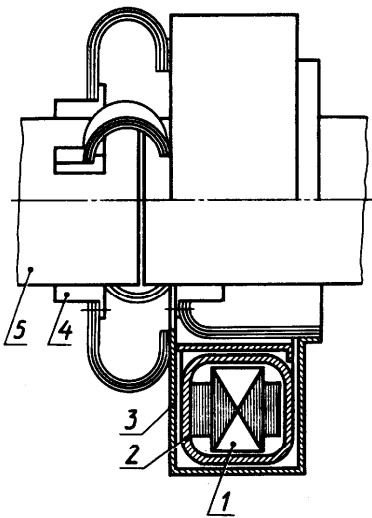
Кольцевой сварочный трансформатор для стыковой сварки труб
